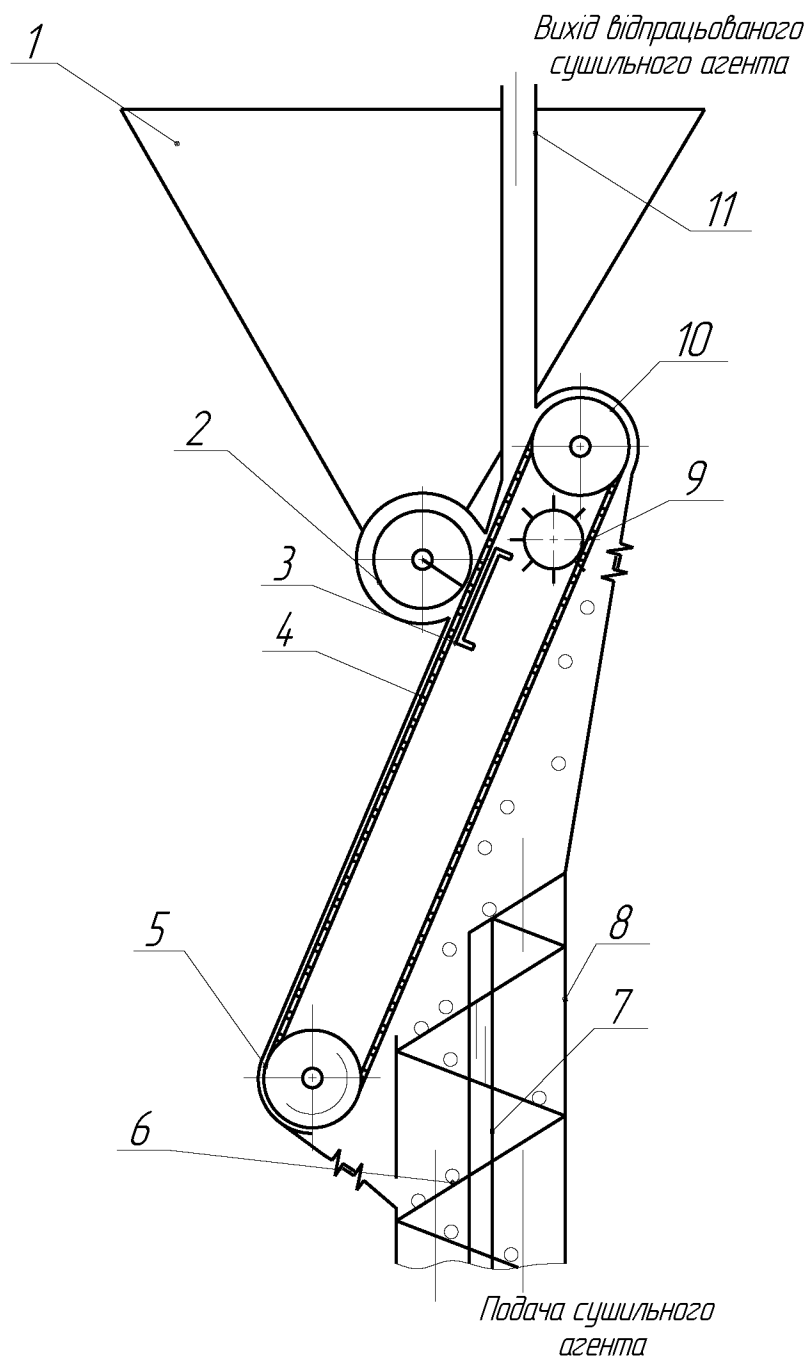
Сушарка-гранулятор: 1-бункер органо-мінеральної суміші; 2- шнек; 3- пластина; 4- транспортер; 5-натяжний барабан; 6-гвинтова поверхня; 7-вал; 8-корпус; 9-валець; 10-привідний барабан; 11-труба відведення відпрацьованого сушильного агента
